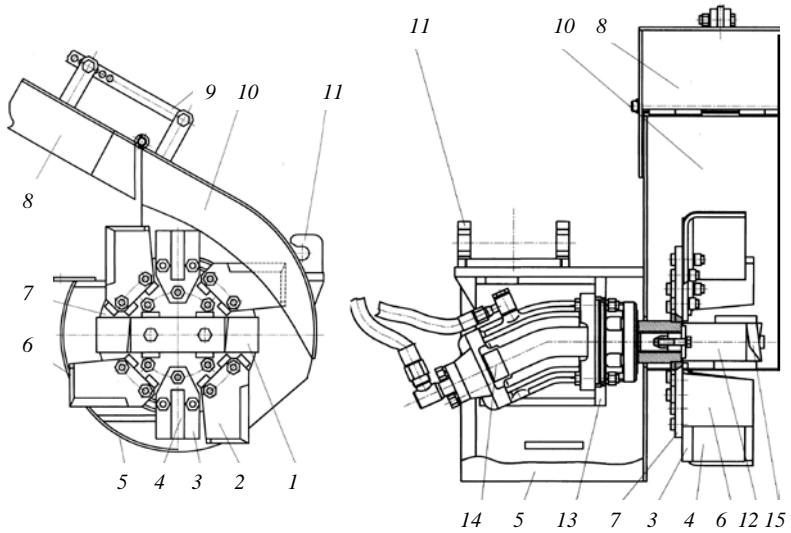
Фрезерный рабочий орган РММ-600 (КОРО-2): 1 – нож; 2 – болты; 3 – основания лопастей; 4 – лопасти; 5 – нижняя часть кожуха; 6 – ножи Г-образные; 7 – диск фрезы; 8 – козырек; 9 – регулируемая тяга; 10 – кожух; 11 – кронштейны; 12 – ступица; 13 – плита кожуха; 14 – гидромотор; 15 – прижимная пластина
